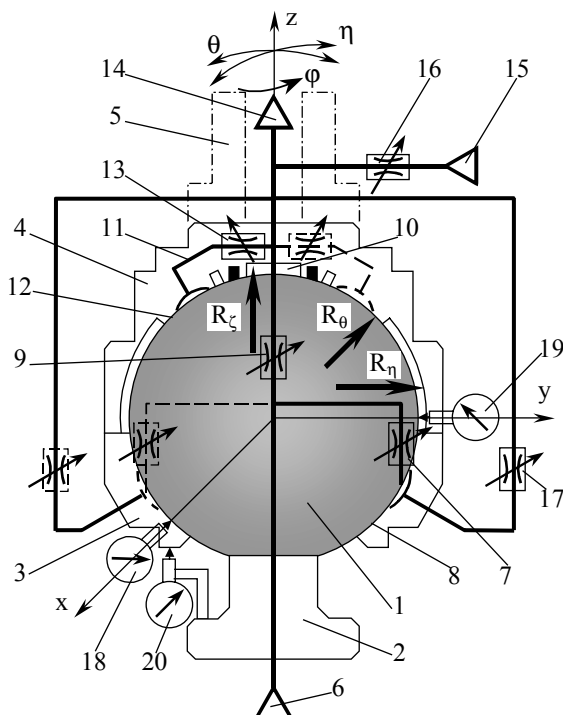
Прецизійний поворотний вузол просторового механізму
